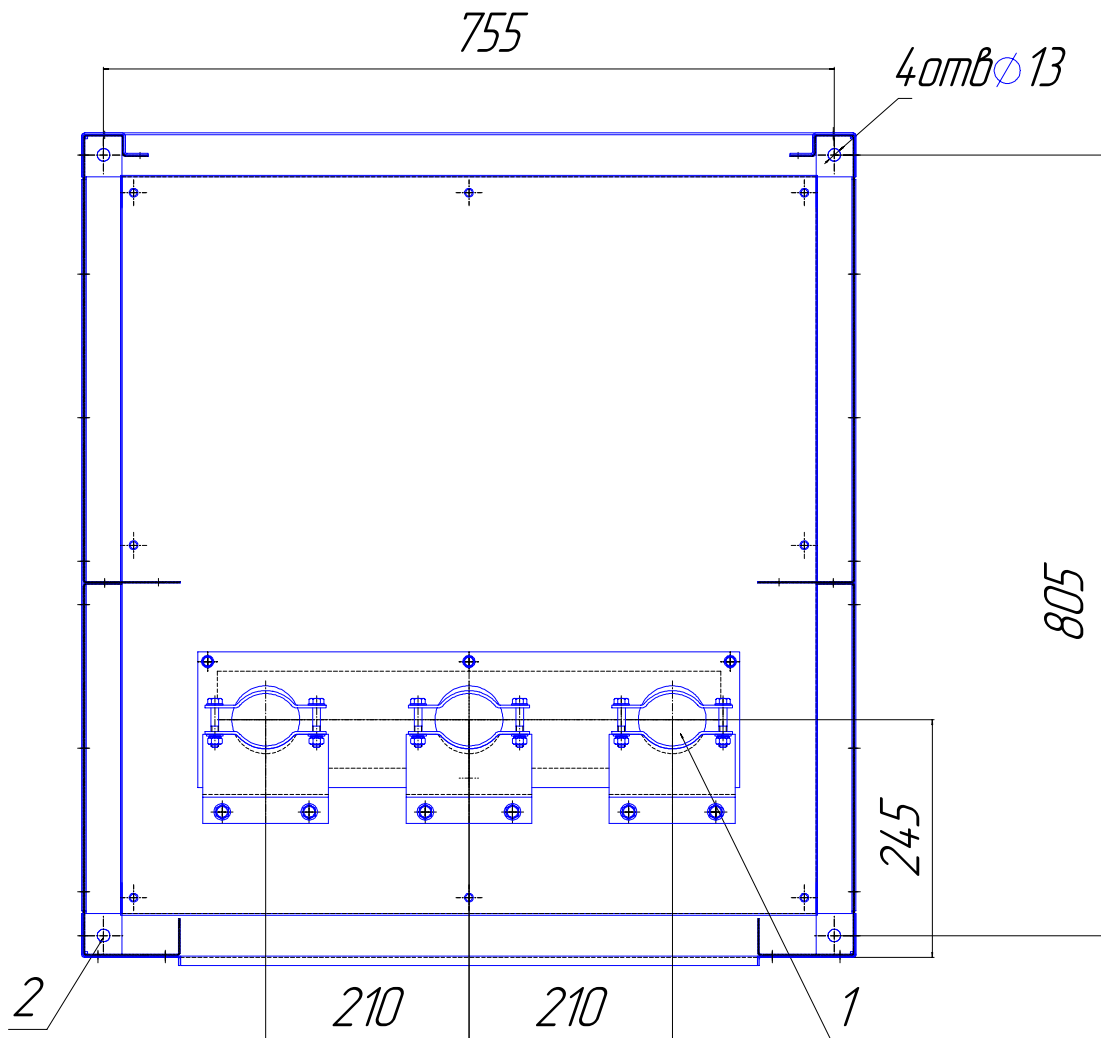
Габаритные и посадочные размеры дна камер КСО-205 КОМПАКТ.
